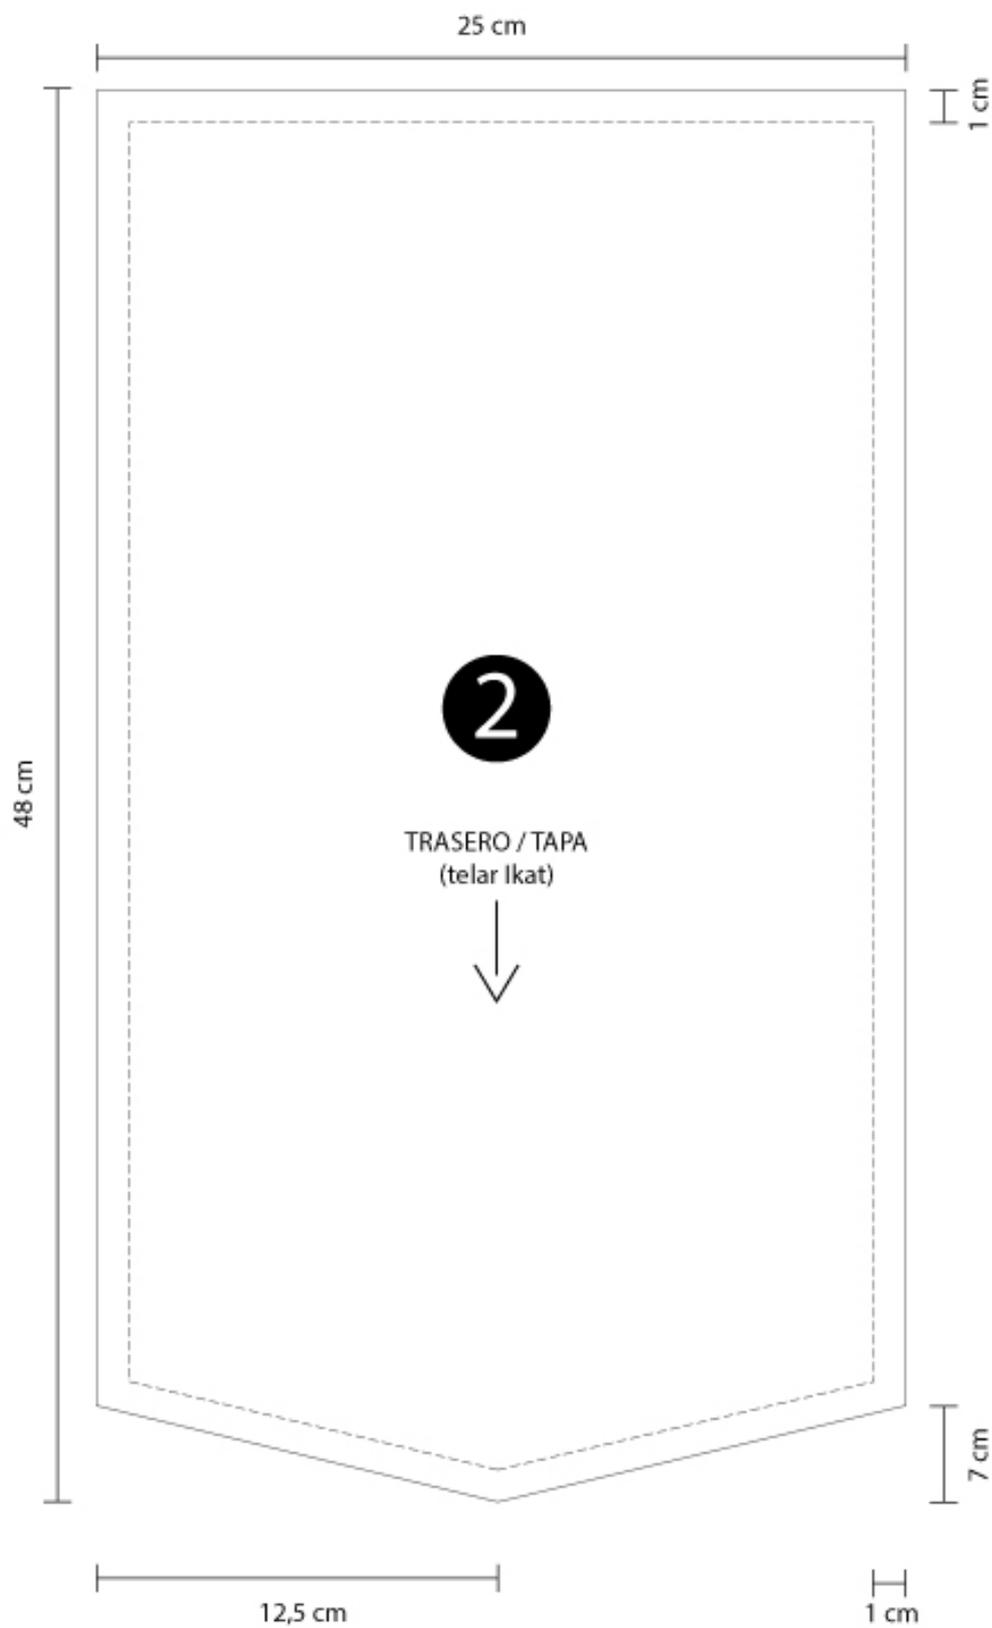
Molde pieza "Trasero & Tapa", escala 1:2.
